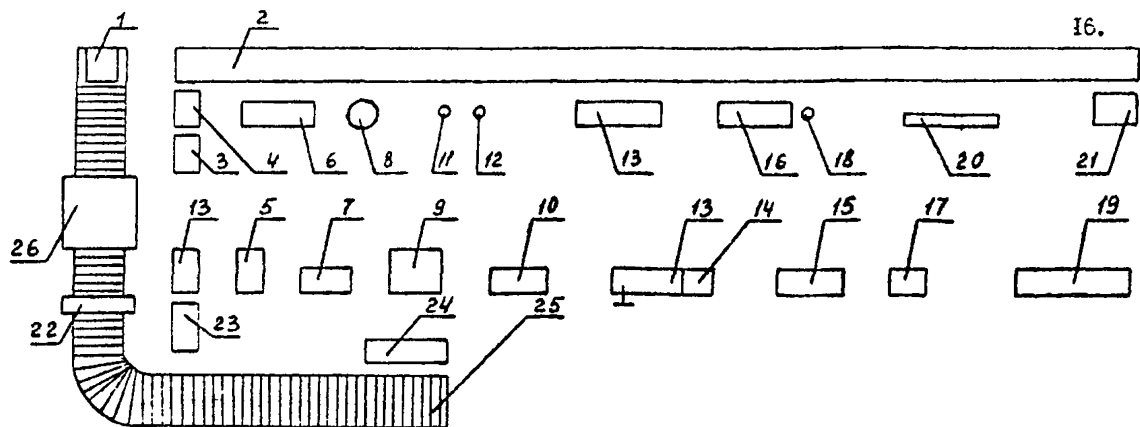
Типовая схема планировки рабочего места сборки двигателя
